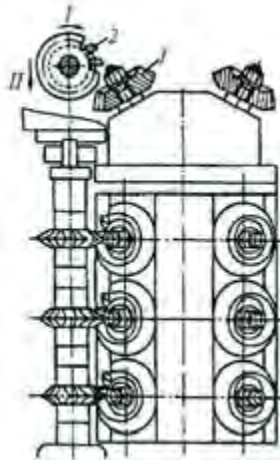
Попереднє нарізування зубців конічних коліс набором фрез
